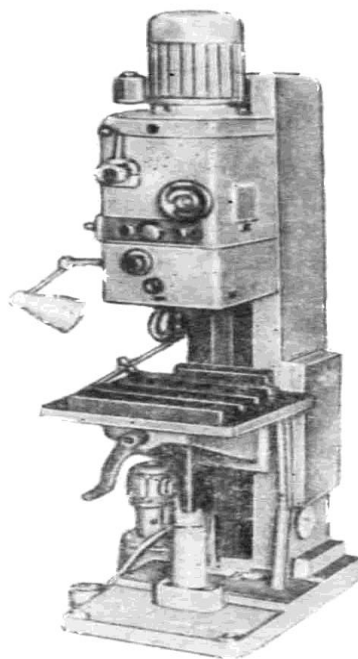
Полуавтоматический резьбонарезной станок модели 2056
